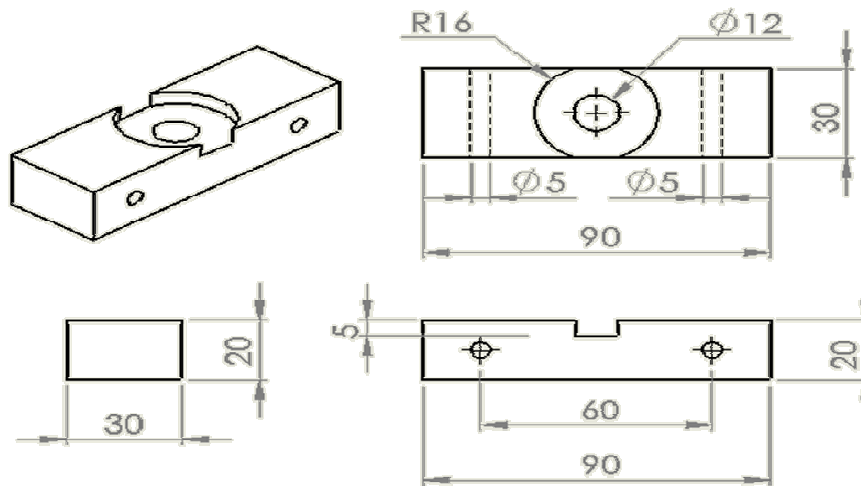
Dimensions du support de l'électrode en millimètre.
